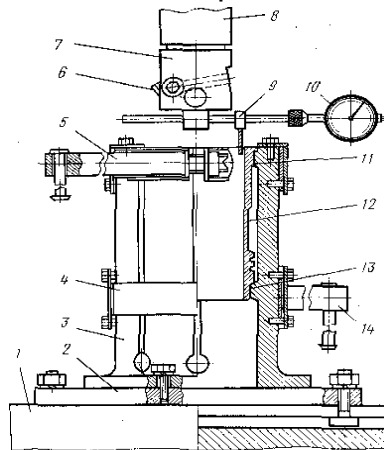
Приспособление для центровки и закрепления гильзы цилиндров на столе расточного станка:
